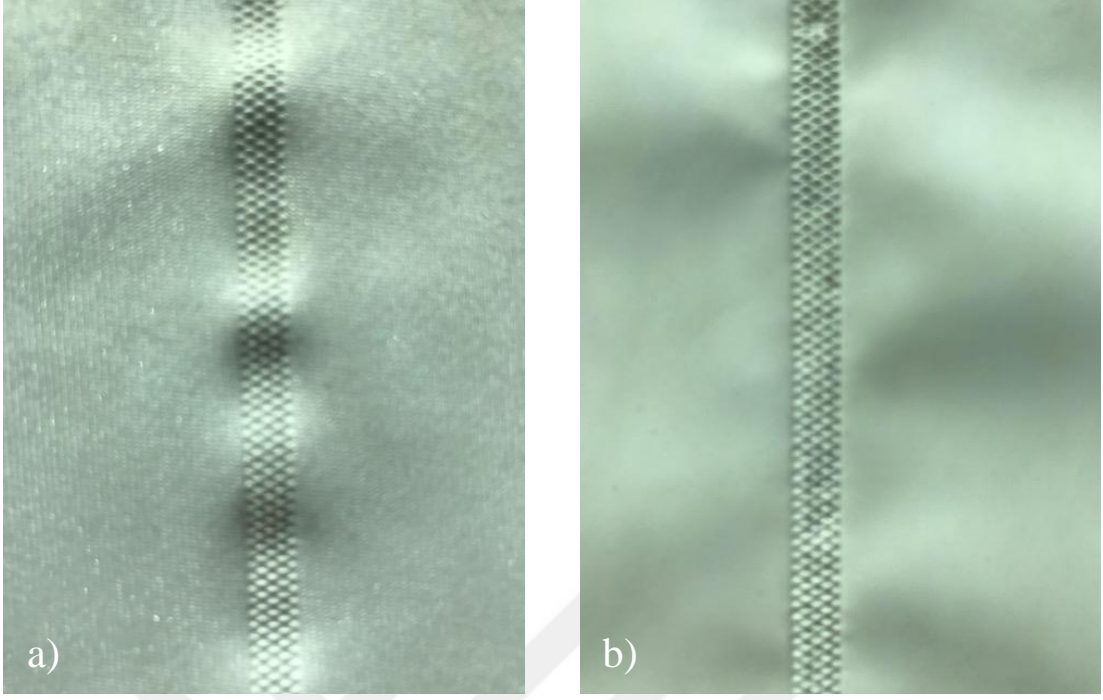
Ultrasonik dikiş makinesinde R1 ile dikilen D3 kumaşının görüntüsü
